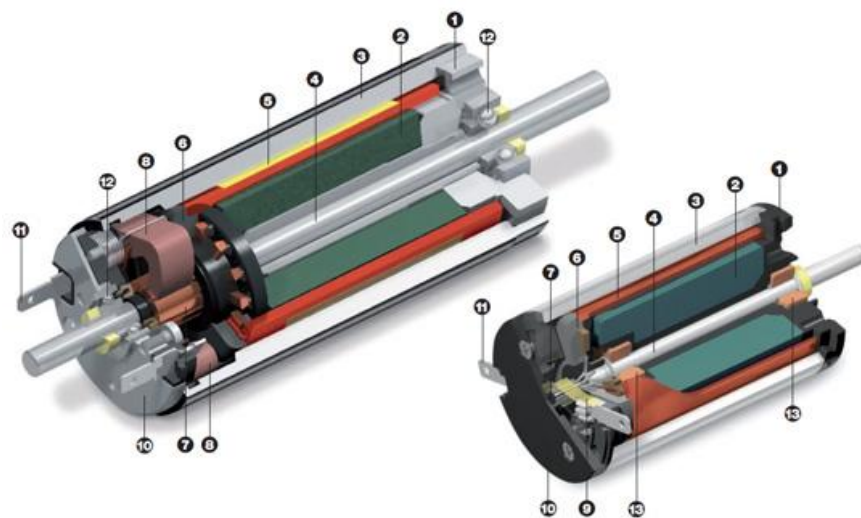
Коллекторный электродвигатель постоянного тока: 1 - фланец, 2 - постоянный магнит, 3 – корпус, 4 – вал, 5 – обмотка, 6 - плата коллектора, 7 – коллектор, 8 -графитовые щетки, 9 - щетки из благородных металлов, 10 – кожух, 11 - электрический контакт, 12 - шариковый подшипник, 13 - металлокерамический подшипник скольжения
